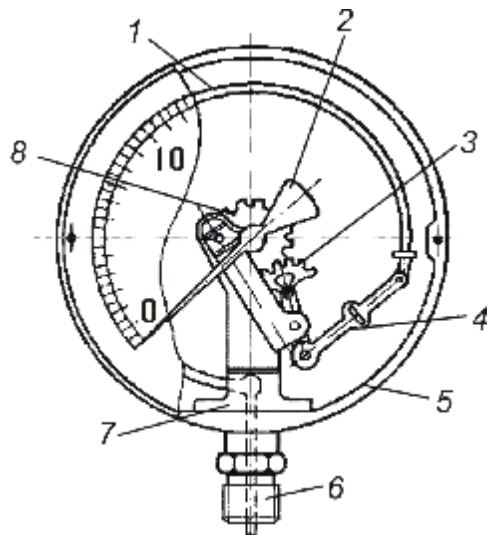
Манометр с одновитковой трубчатой пружиной: 1 – трубчатая пружина; 2 – стрелка; 3 – зубчатый сектор; 4 – тяга; 5 – корпус манометра; 6 – ниппель; 7 – основание манометра; 8 – трибка
